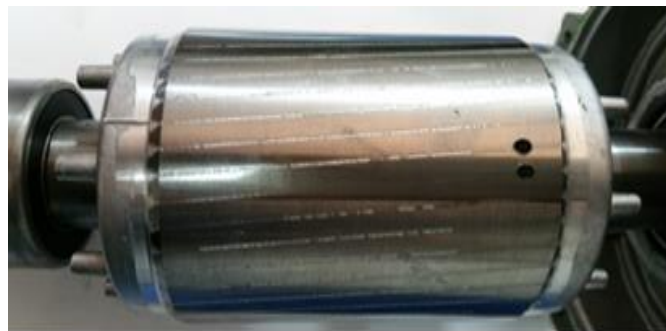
Rotor avec deux barres adjacentes cassées d'une machine à induction
